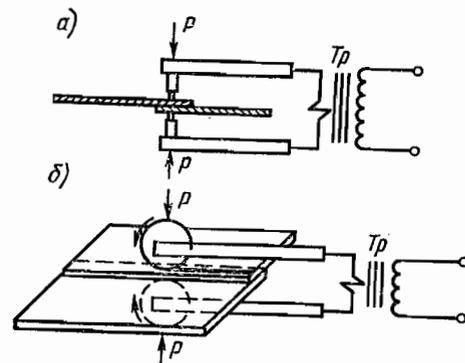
Схема точечной (а) и роликовой (б) сварки
